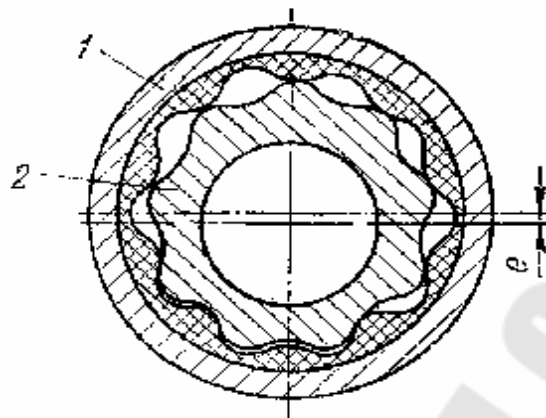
Поперечное сечение рабочих органов винтового двигателя: 1 – статор; 2 – ротор
